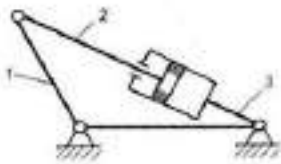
Кулисный механизм: 1 — кривошип; 2 — шатун; 3 — поршень
